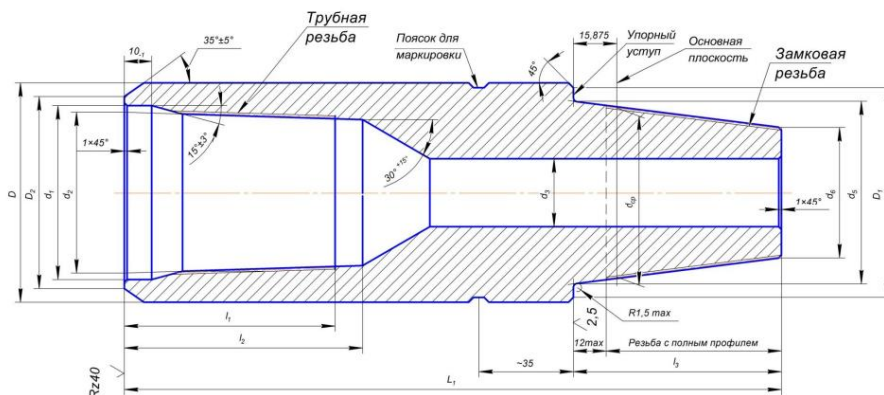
Чертёж ниппеля замков типов ЗН, ЗШ и ЗУ
